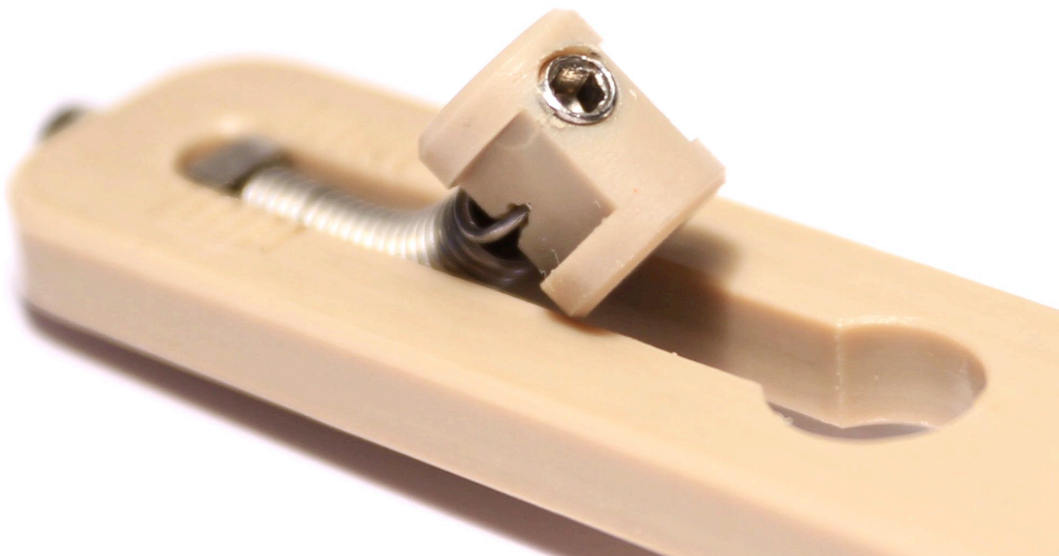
Federschlitten vor Einsetzen in die Gleitschiene mit sichtbarer Fixierung der Zugfeder sowie Gewindestift zur K-Draht Fixierung.
